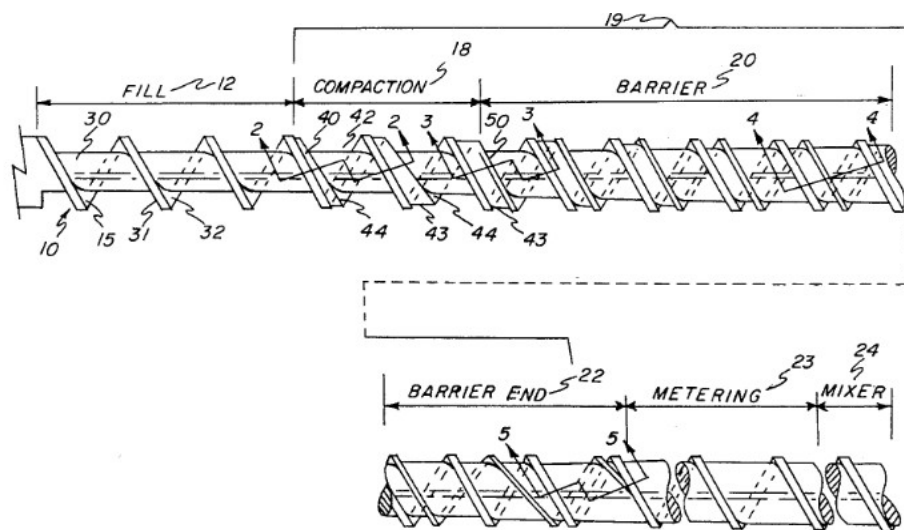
Конструкція черв'яка екструдера з бар'єрною зоною
